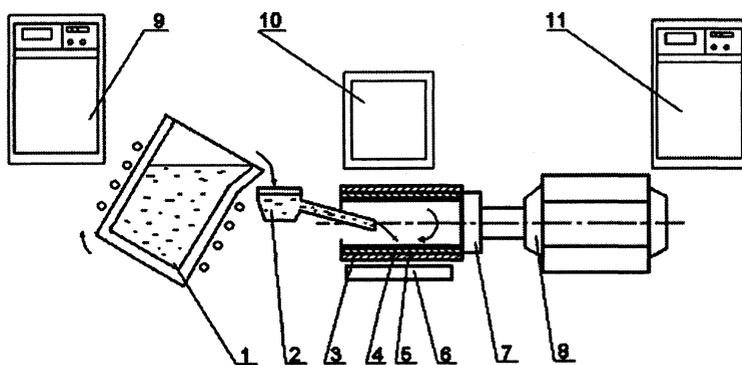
Схема установки с раздельным плавлением шихты и подогревом стальной основы: 1 – индукционная печь; 2 – заливочный желоб; 3 – стальная заготовка; 4 – наплавленный слой; 5 – флюс; 6 – индуктор; 7 – устройство крепления заготовки; 8 – привод вращения заготовки; 9 – высокочастотный генератор №1; 10 – вторичный трансформатор; 11 – высокочастотный генератор №2
